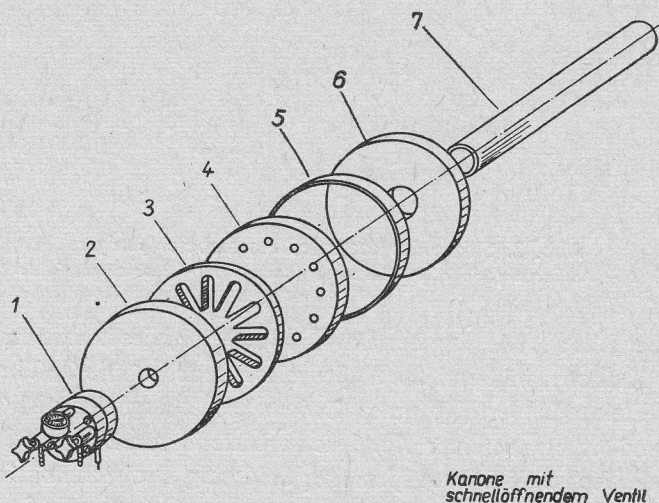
Explosionszeichnung der Plasmaquelle [1]
